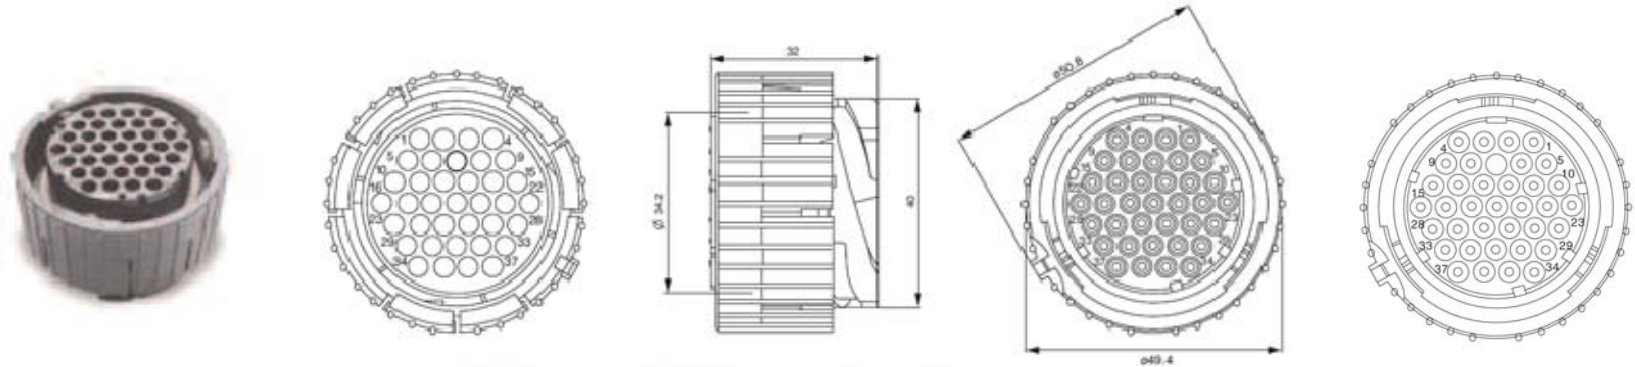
Rück- und Frontansicht ITT-Cannon / Rear and Front View ITT-Cannon
